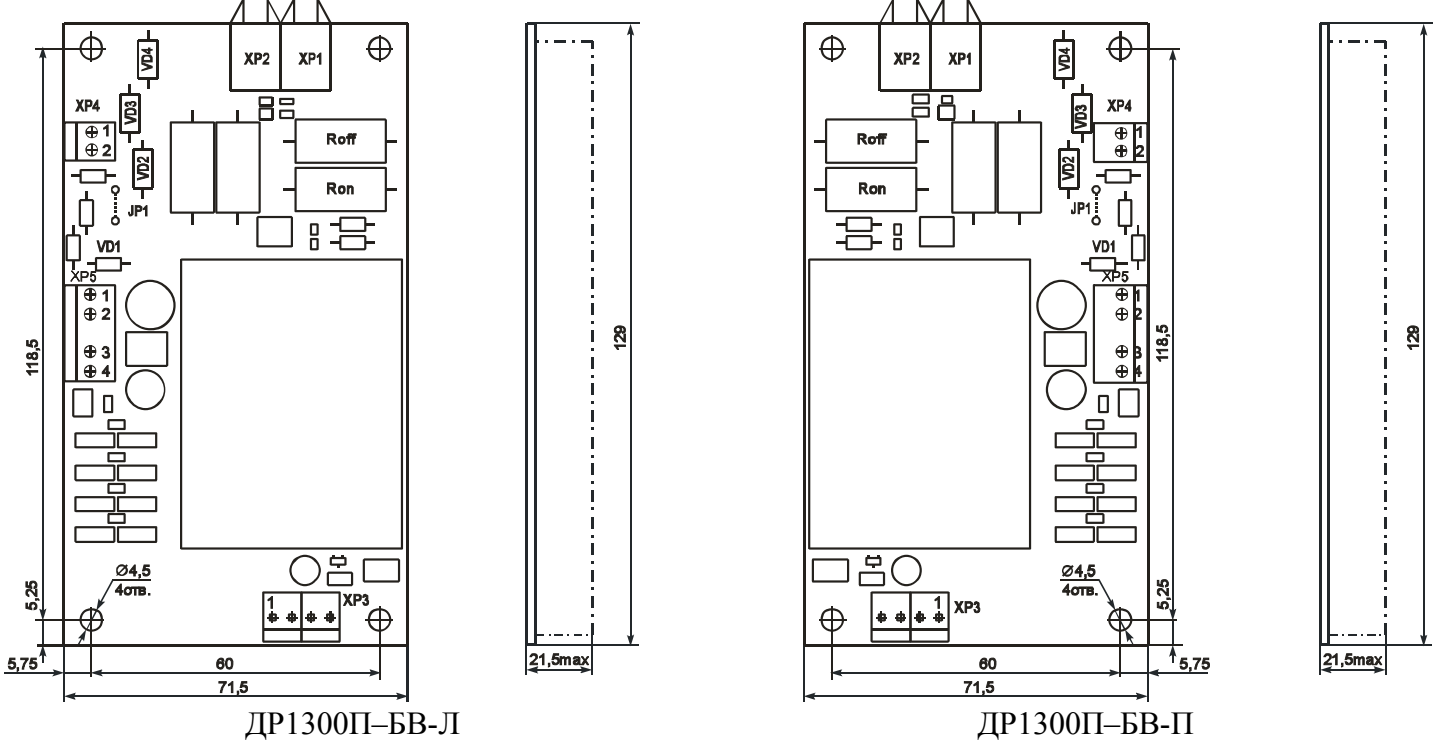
Габаритные и присоединительные размеры драйверов
